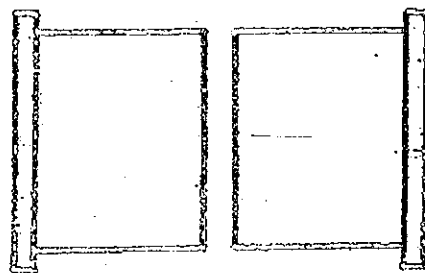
กงล้อแบบแยกชิ้นได้ (REMOVABLE FLANGE หรือบางทีก็เรียก DEMOUNTABLE FLANGE WHEEL) สองรูปแบบเป็นแบบคอดกลาง สองรูปร่าง เป็นแบบเรียบ
